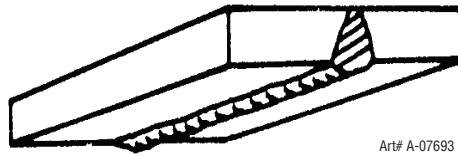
Position au plafond, soudure bout à bout
